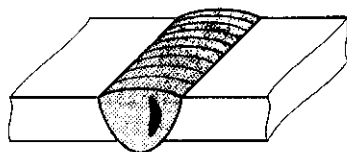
Усадочная раковина в металле сварного шва
